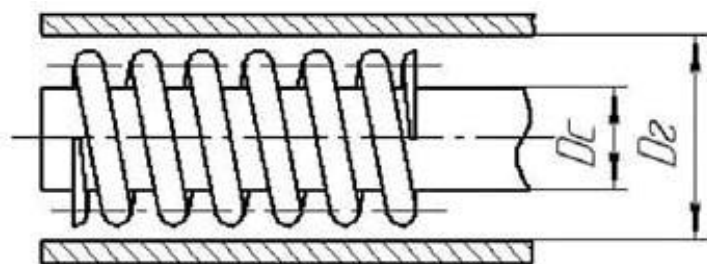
Оправки и гильзы цилиндрических винтовых пружин
